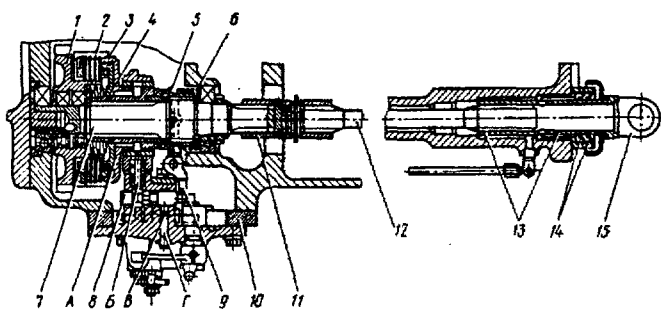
Привод переднего ведущего моста тракторов МТЗ-102: 1 – шестерня ГПМ; 2 – ГПМ; 3 – барабан; 4 – поршень; 5 – полумуфта; 6 – пружина; 7 и 12 – валы; 8 – золотник крана; 9 – вилка; 10 – кран; 11 – соединительная втулка; 13 – биметаллические втулки; 14 – манжеты; 15 – скользящая вилка; А – рабочая полость цилиндра ГПМ; Б, В и Г – каналы
